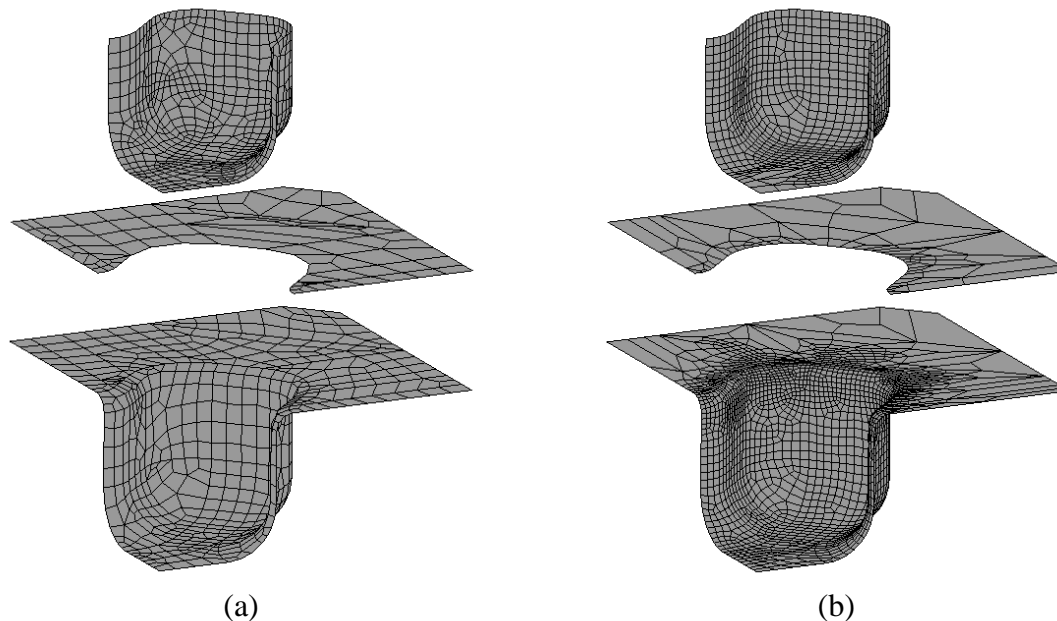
Discretizações não estruturadas utilizadas na construção dos modelos: (a) A-1273; (b) CE-3096.
